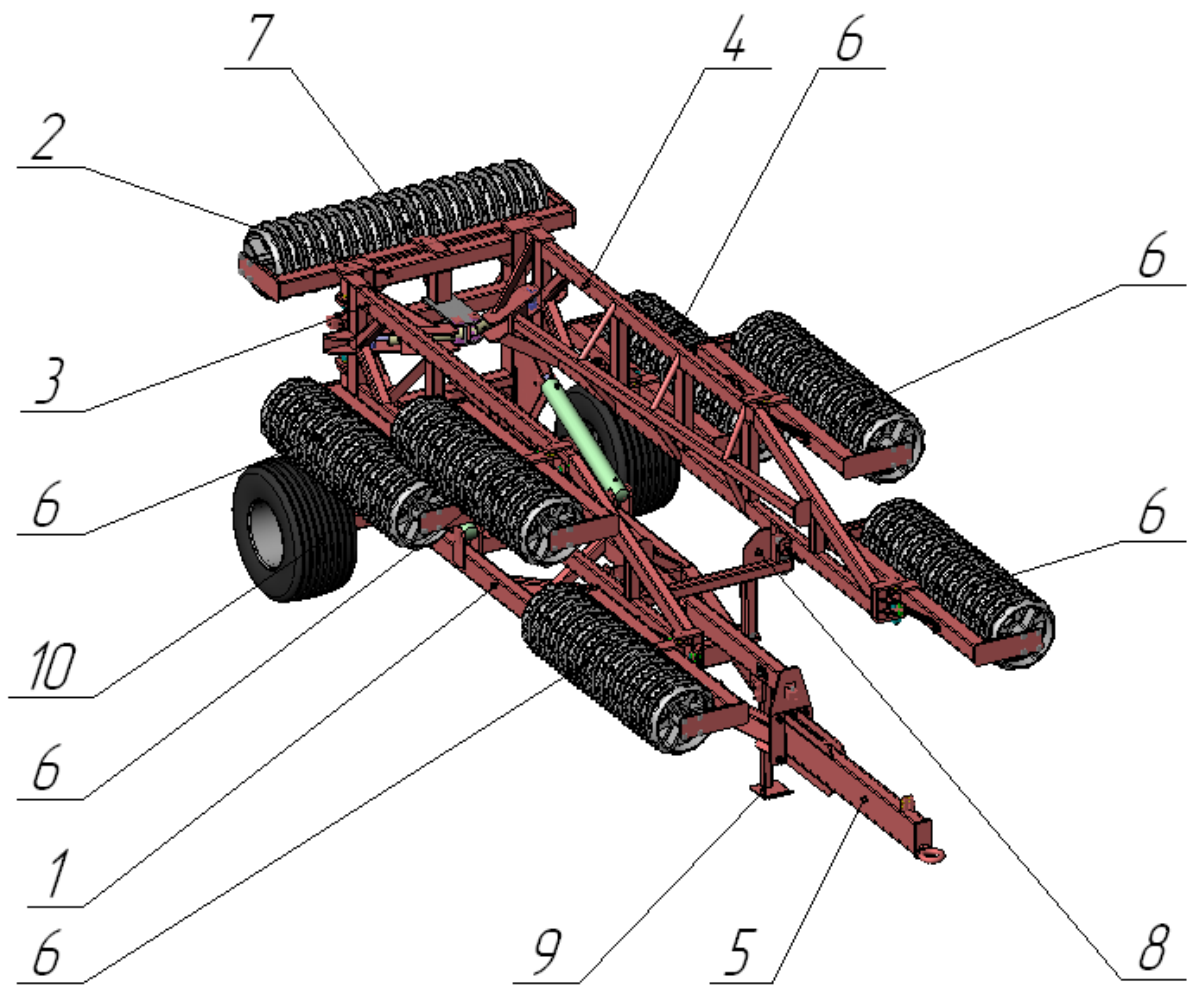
Общий вид катка кольчато-зубчатого Булава КЗ-12,4
